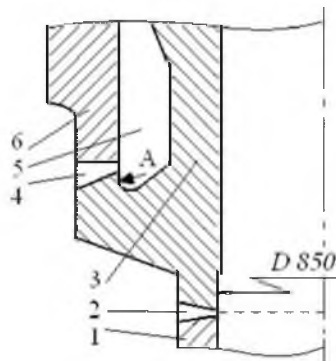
Фрагмент узла сварного соединения: 1 – ГЦТ; 2, 4 – сварной шов; 3 – коллектор ПГ; 5 – “карман”; 6 – патрубок ПГ.
